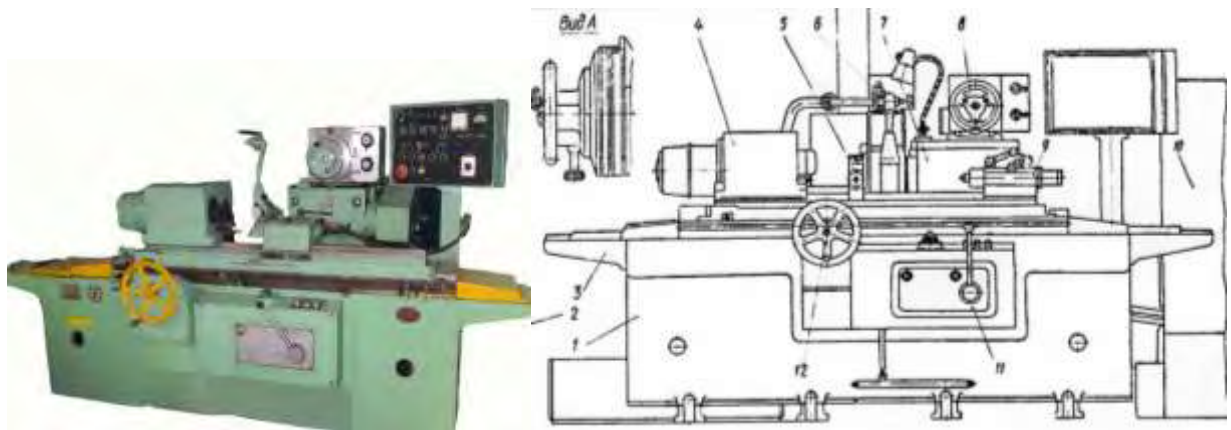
Круглошлифовальный полуавтомат 3М151
